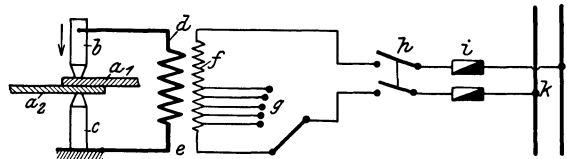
Schaltung und Stromzuführung bei Punktschweißmaschinen.
